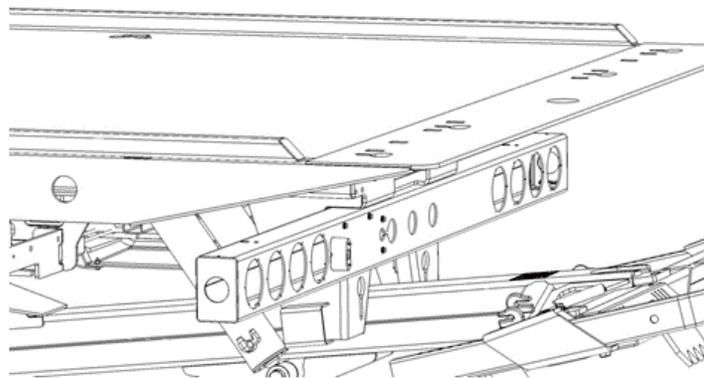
RAILS INSTALLÉS À 1 PO AU-DESSUS DU PLANCHER
